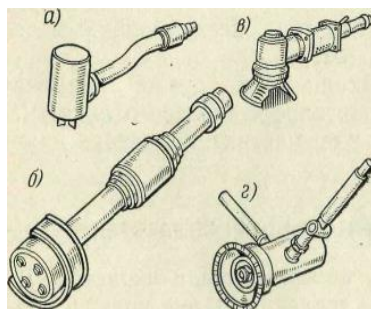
Механизированный инструмент для очистки и подготовки поверхностей к окраске: а – молоток пневматический; б – шарошка пневматическая; в – УПЩР-1; г – ТПЩ-1
